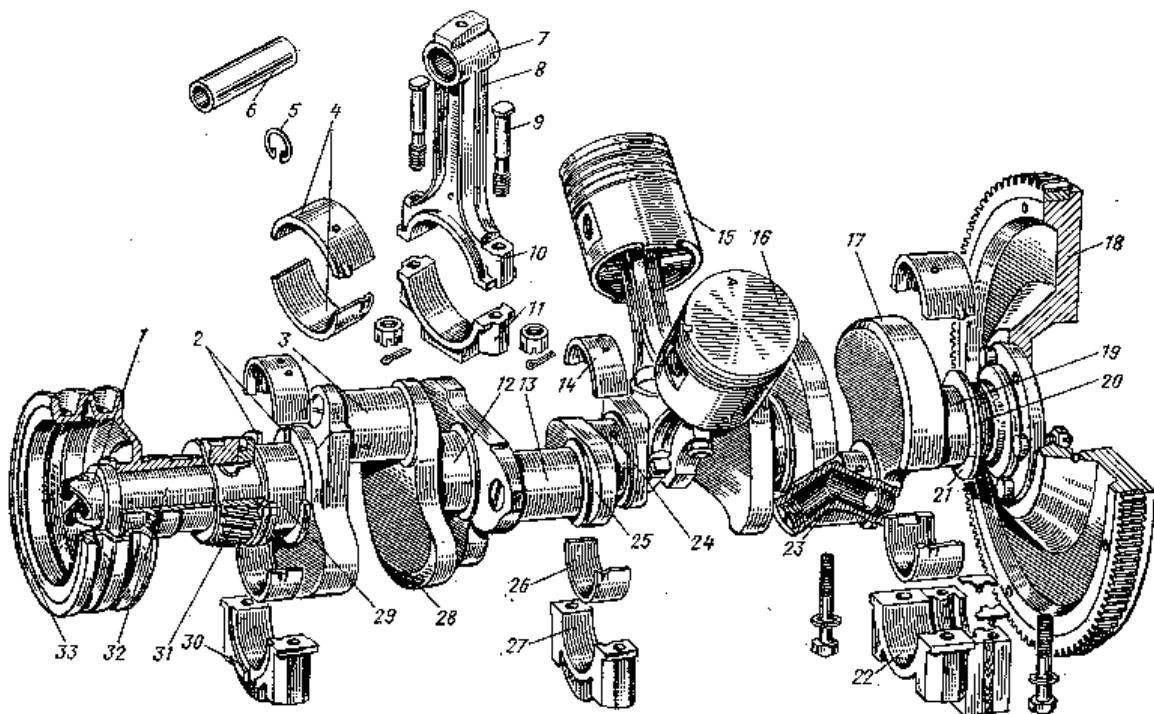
Коленчатый вал и шатунно-поршневая группа
